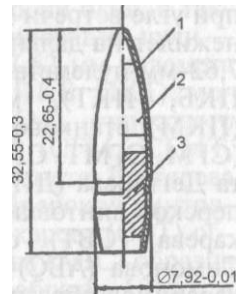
7,62-мм винтовочный патрон с пристрелочно-зажигательной пулей ПЗ:
